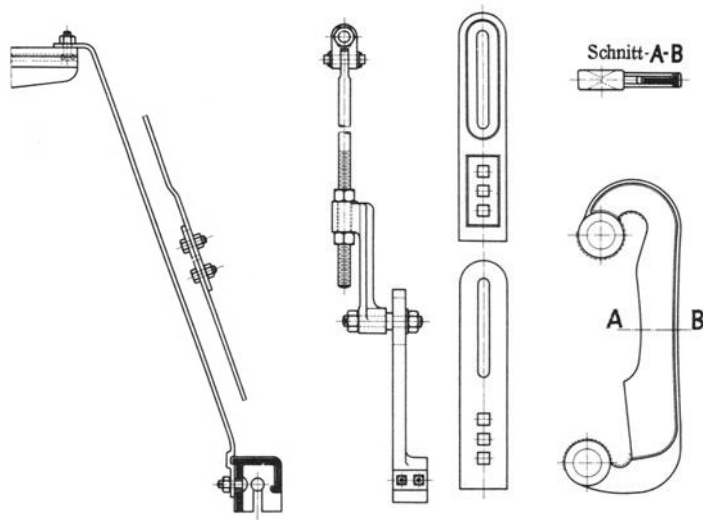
Details der Horák'schen Schaftmaschine (Stütze der Konsole Y, Kurbel mit Zugstange V, Ev. Verlängerung des dreiarmigen Hebels R', Zugstück Z' in Draufsicht und Schnitt). Alles in Abb. 52.
